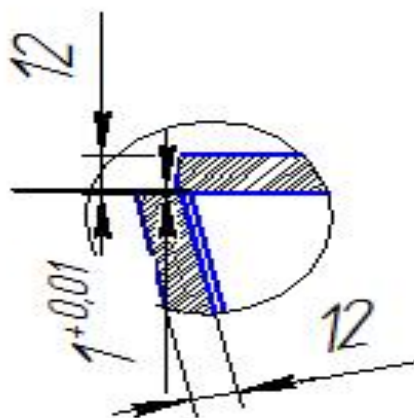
сварное соединение У1 для механизированной сварки в CO<sub>2</sub> по ГОСТ 23518-79
